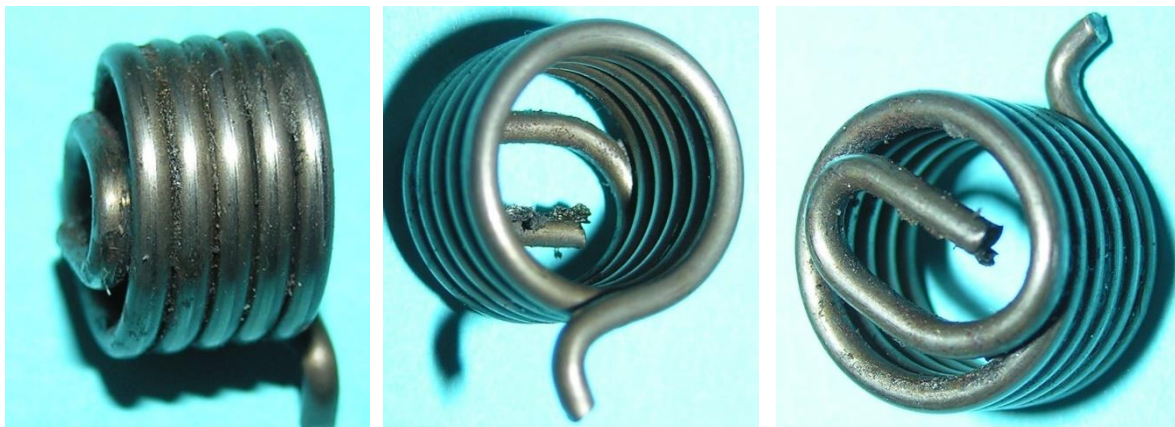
Ansichten der Druckfeder: a) Ausschließlich auf Torsion beanspruchte Druckfeder, b) Hakenende, b) Schlaufenende
